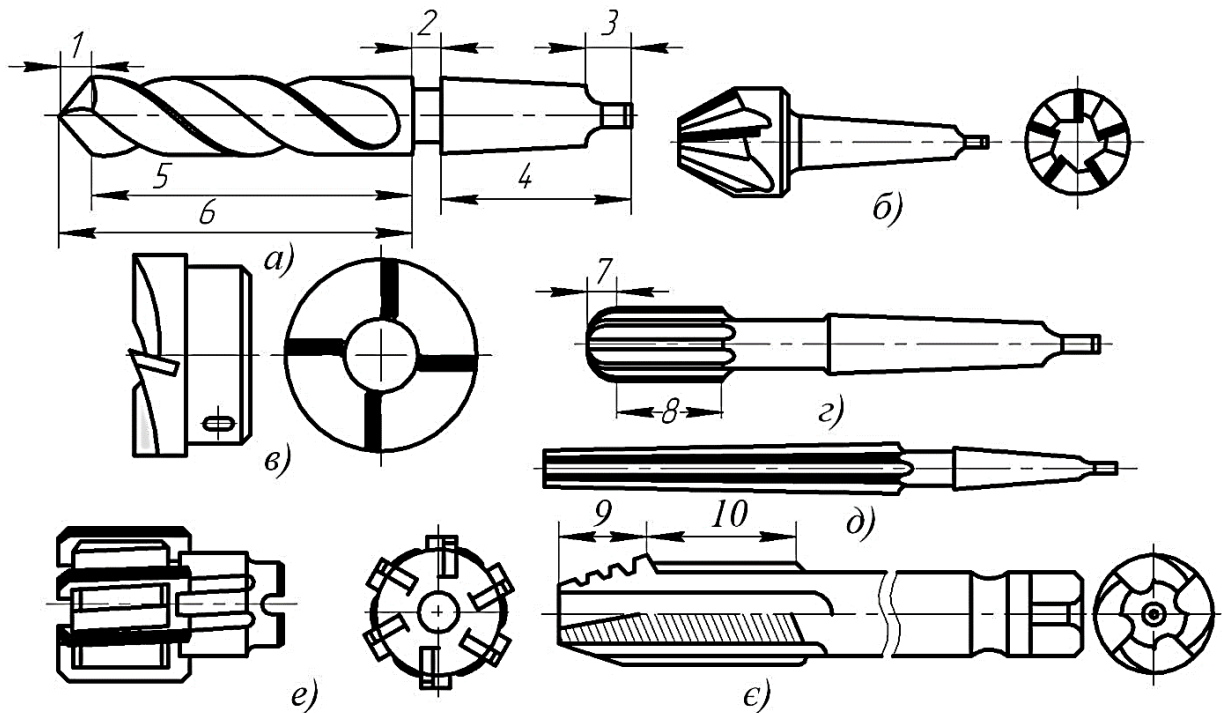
Інструменти для обробки отворів на свердлильних верстах:
